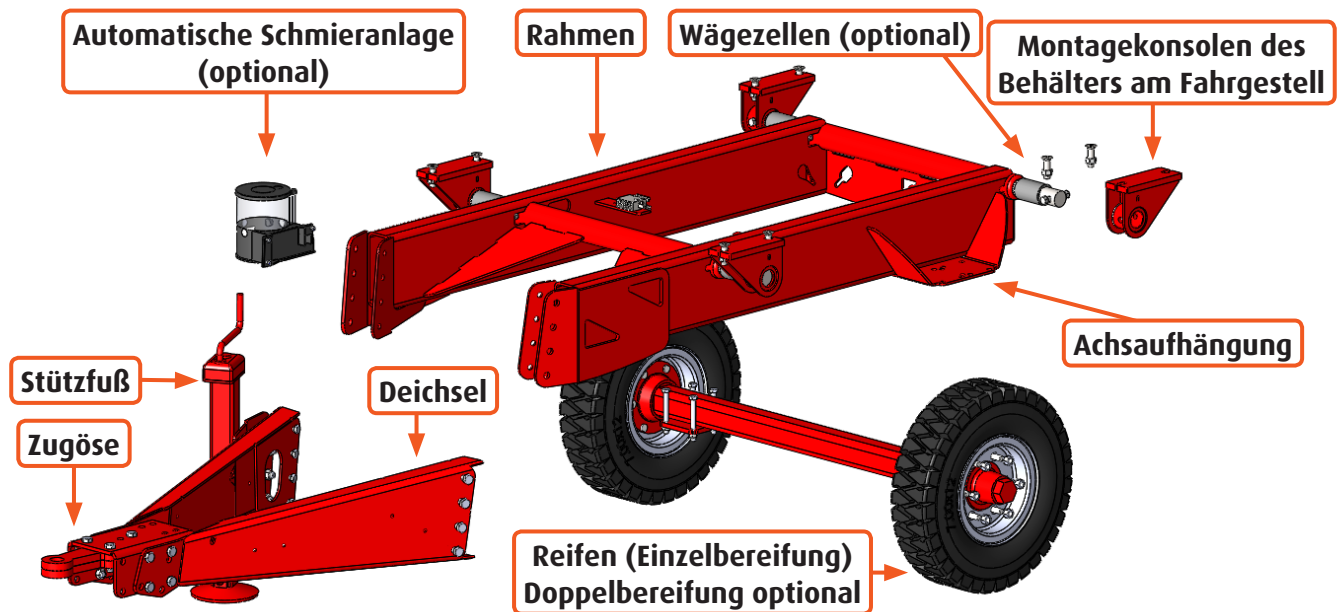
Fahrgestellaufbau Biga mit Einzelachse
